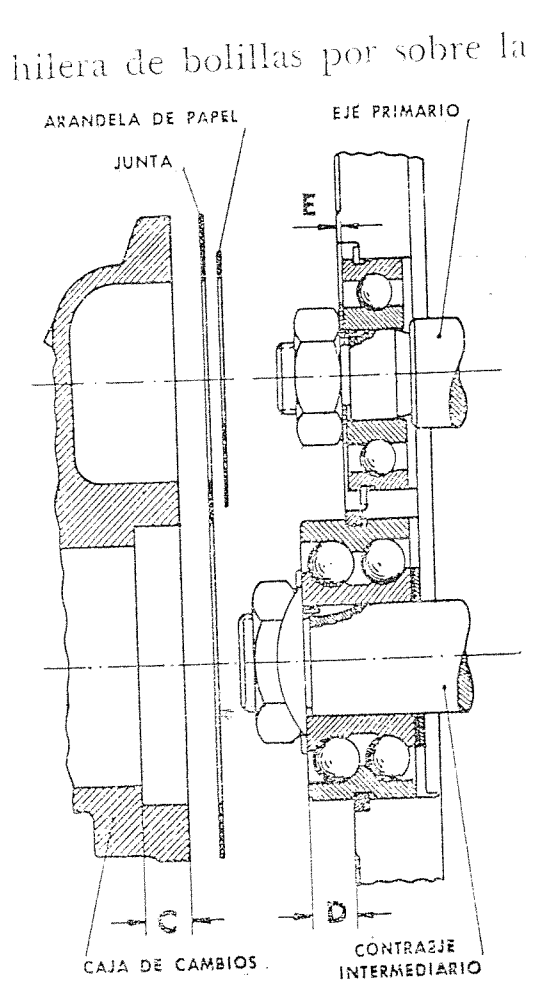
Tensión previa de los cojinetes a bolillas de la caja de engranajes.
